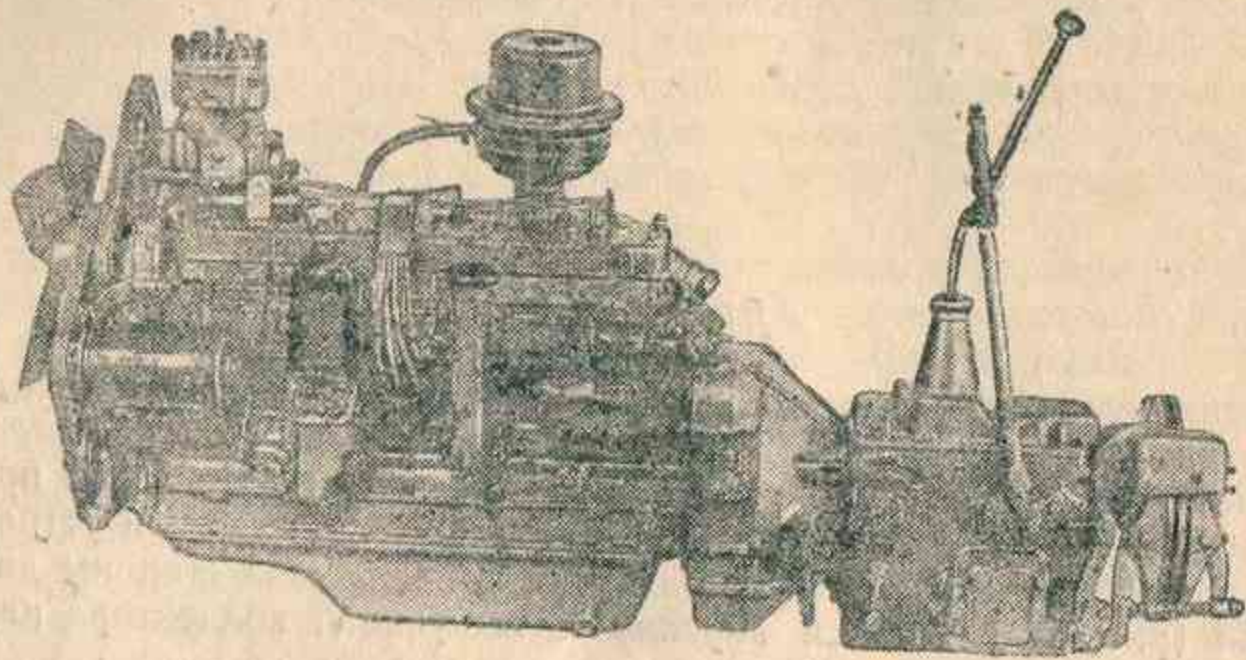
Двигатель со сцеплением и коробкой передач в сборе (вид слева)
